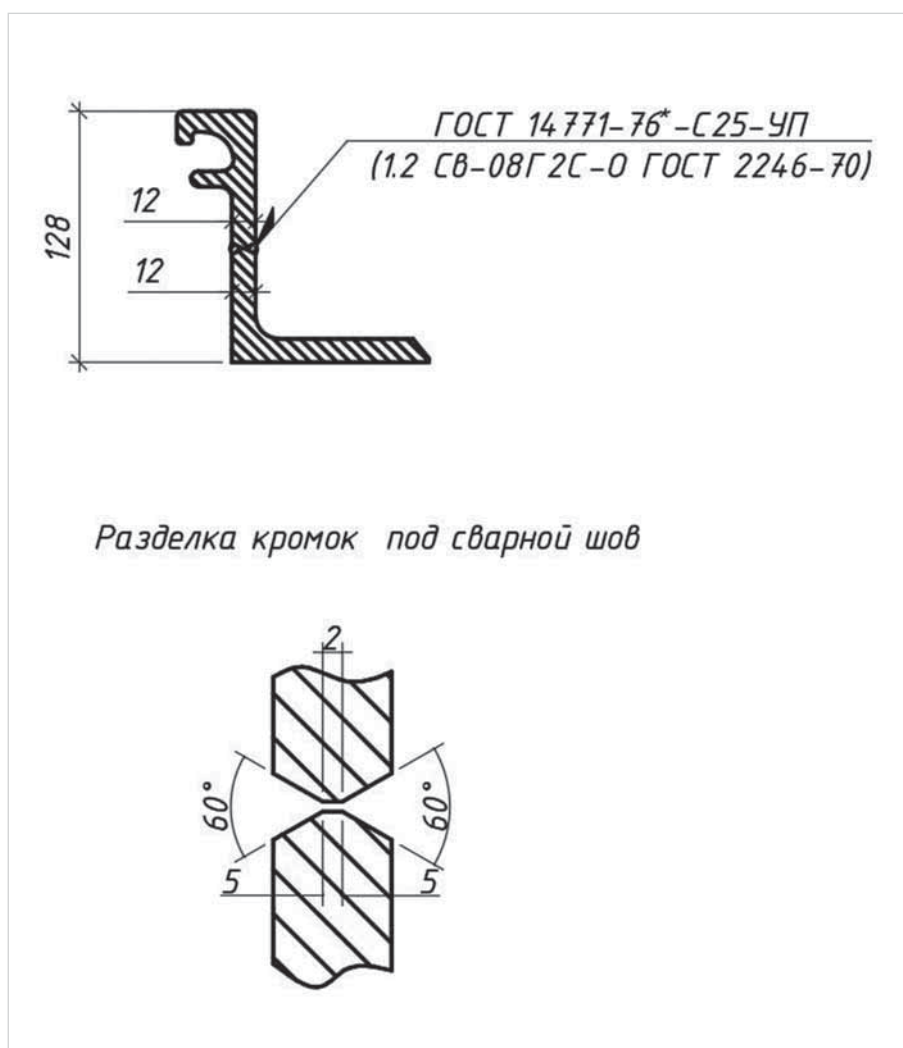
Схема сварного шва профиля окаймливания
